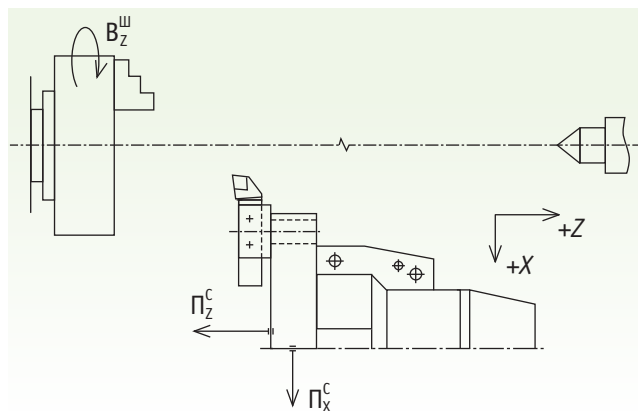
Формообразующие движения рабочих органов токарного станка 16Р35Ф3
